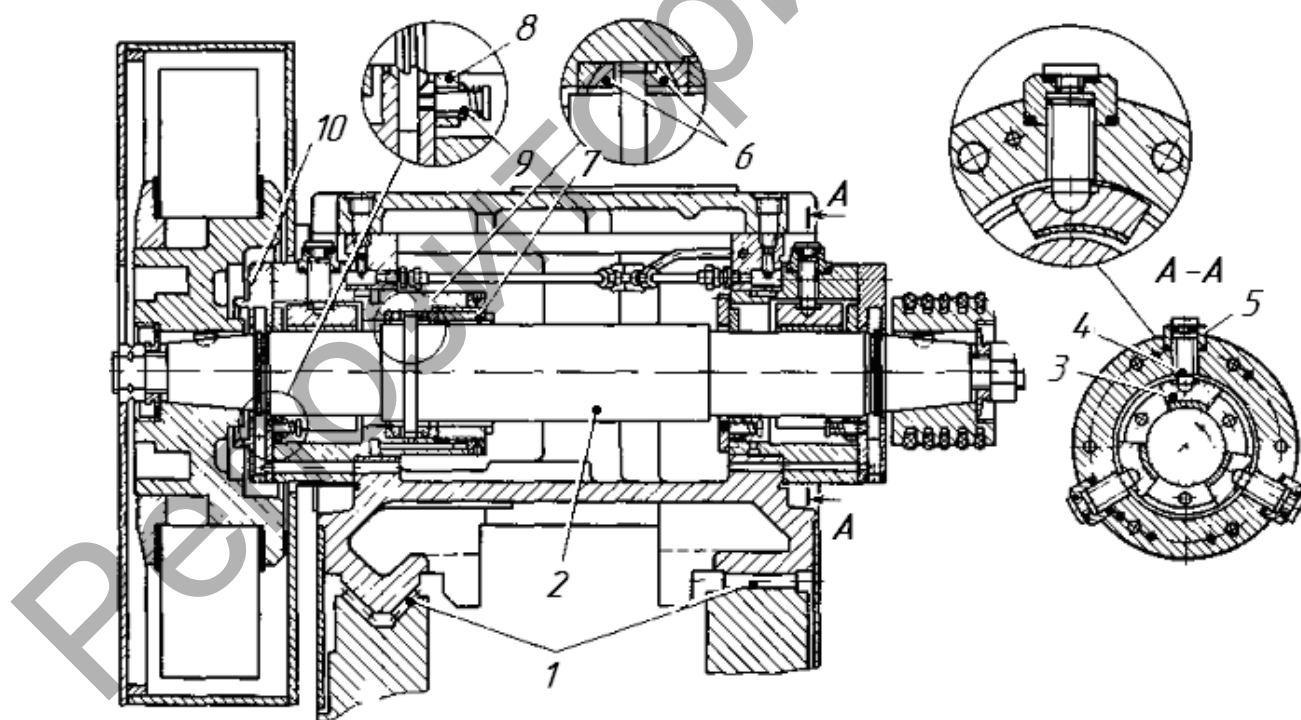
Шлифовальная бабка станка 3М151П
